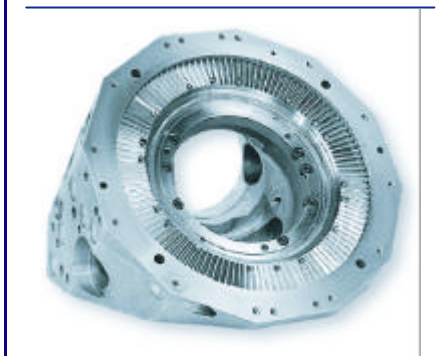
Чугунный корпус шпиндельной угловой головки обрабатывающего центра
